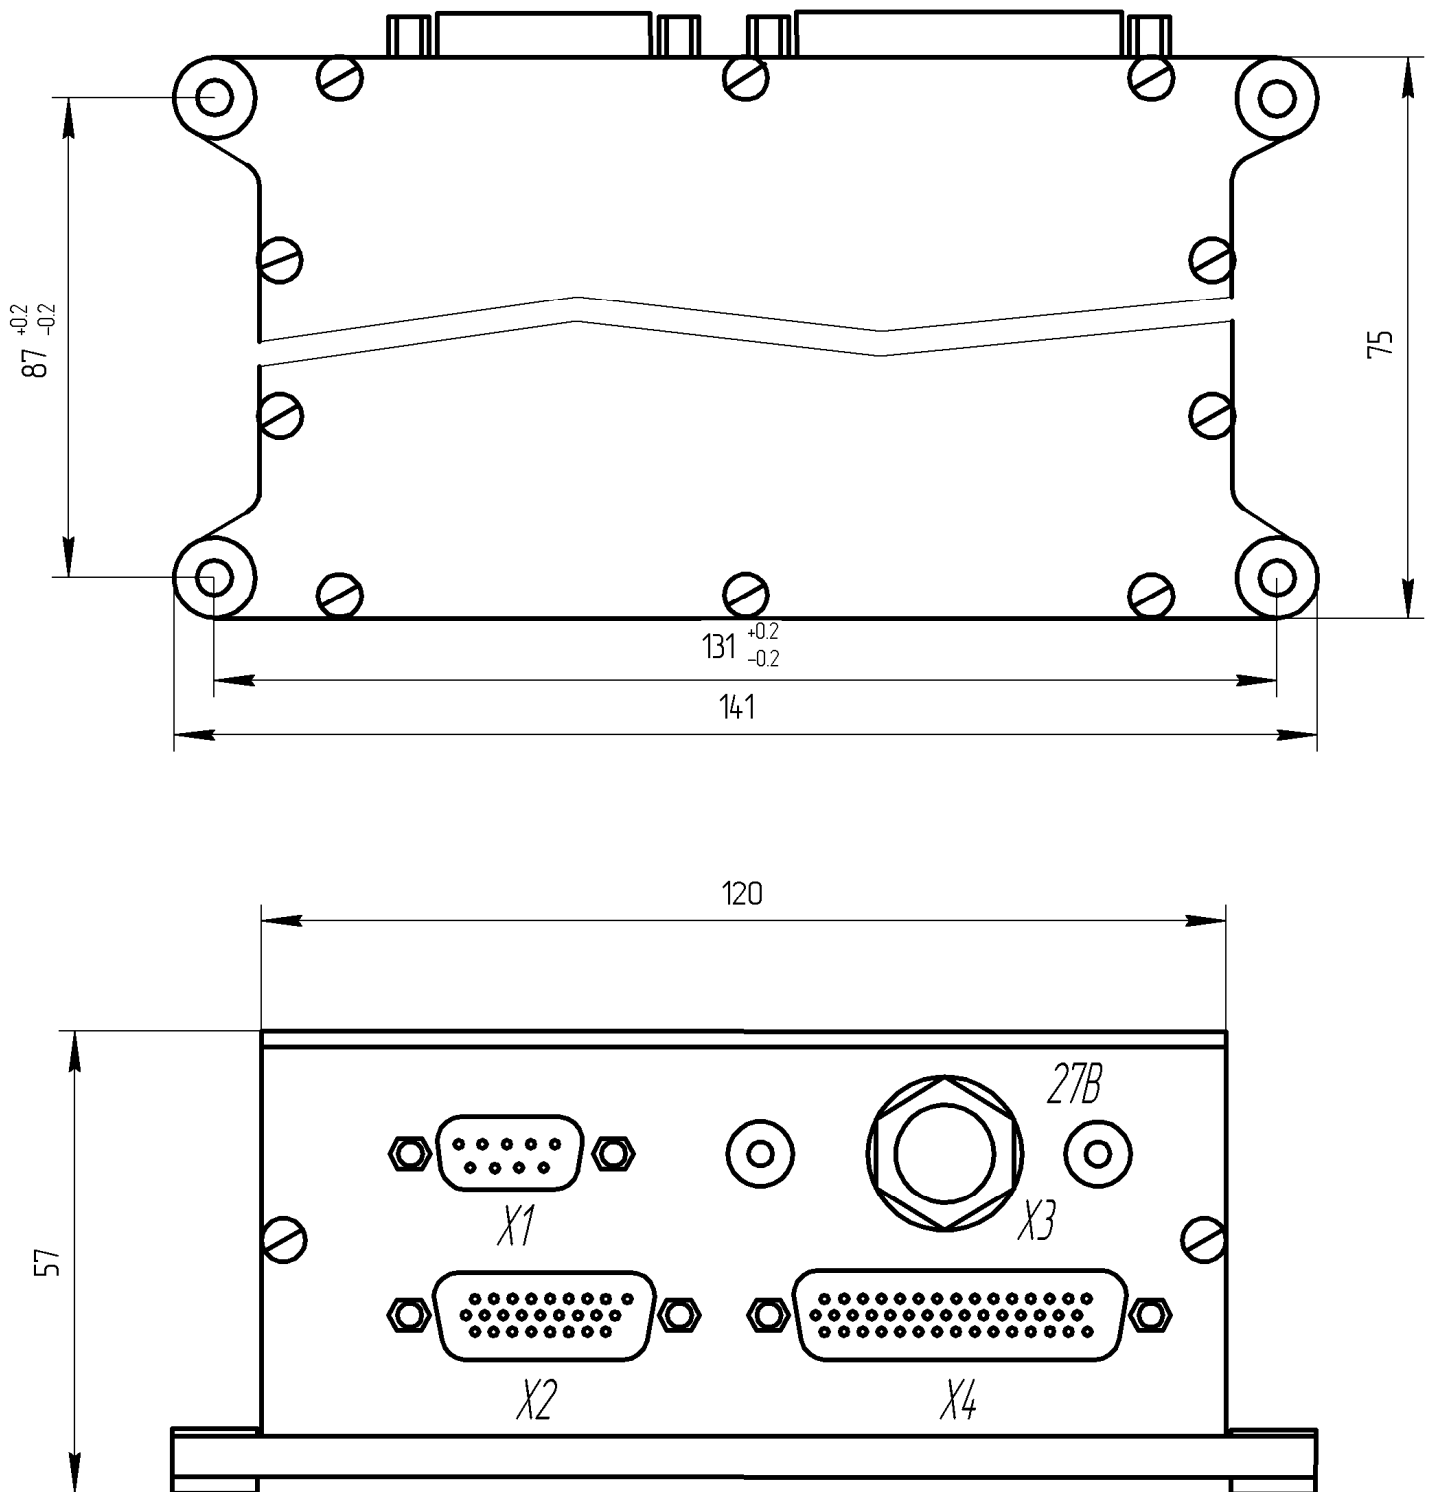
Габаритные установочные размеры концентратора КПИ-1.
